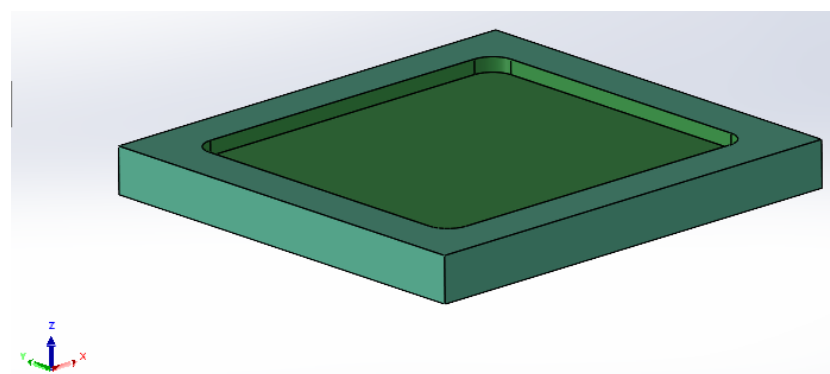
Representação isométrica do molde superior/inferior da placa de HDPE (*Solidworks*).
